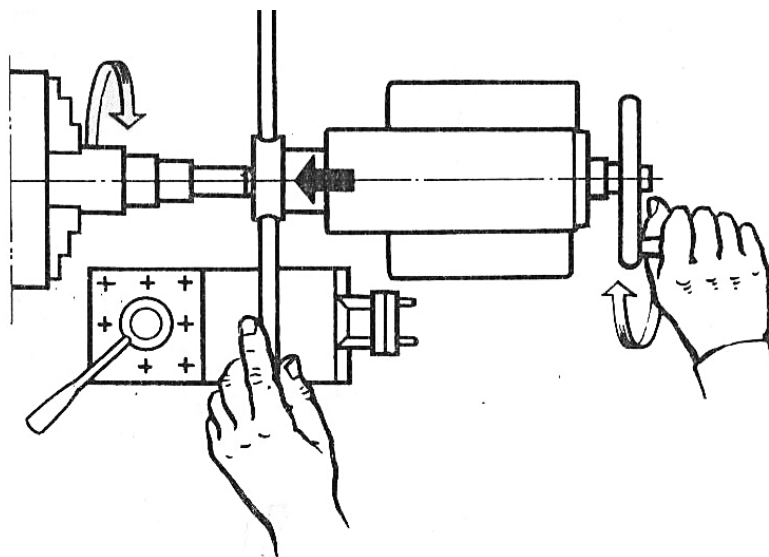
Нарезание резьбы плашкой на токарном станке
